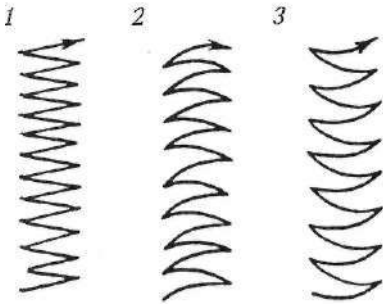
Траектория сварки на подъем корневого и первых за-
